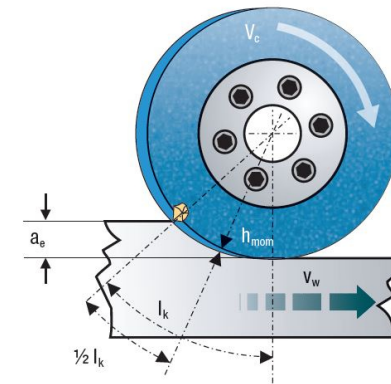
Поверхня контакту шліфувального круга та заготовки
